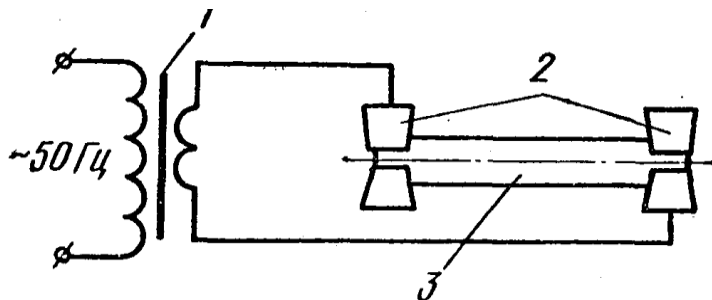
Принципова схема електроконтактного способу нагрівання заготовок
